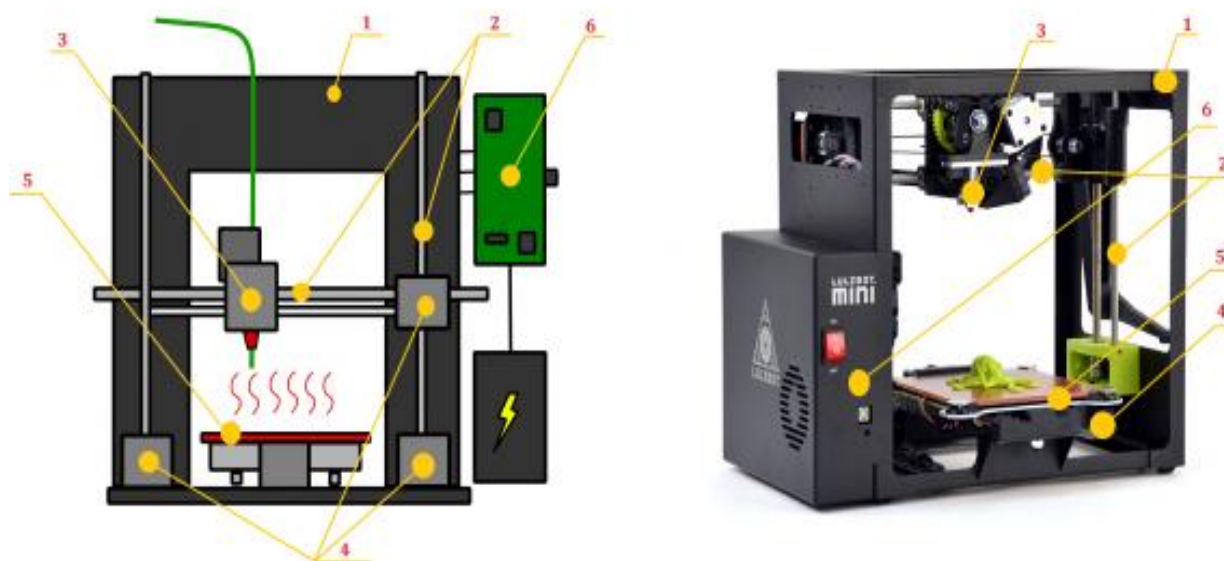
Конструкция 3Д принтера [4]: 1-корпус. 2-направляющие. 3- печатающая головка (экструдер). 4- шаговые двигатели. 5- рабочая платформа.6- электроника.
